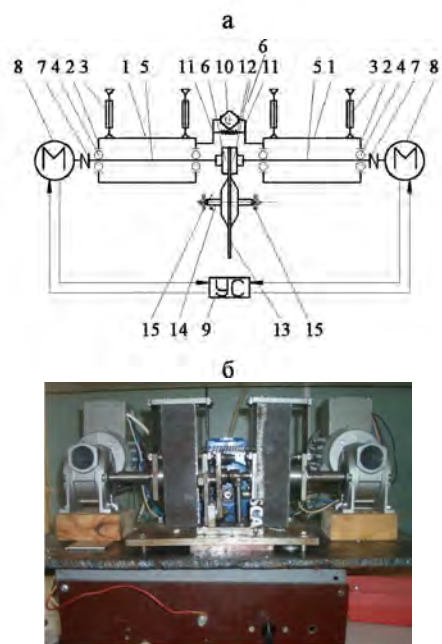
Схема установки для виброударной обработки заготовок дисков: а – конструктивное исполнение установки для виброударной обработки; б – ее общий вид; 1 – виброударная система; 2 – корпус; 3 – плоские пружины; 4 – подшипники качения; 5 – вал; 6 – деформирующий инструмент; 7 – пальцевая муфта; 8 – двигатель; 9 – устройство синхронизации; 10 – кулачок; 11 – кронштейн; 12 – пружина; 13 – обрабатываемая заготовка; 14 – оправка; 15 – опоры
